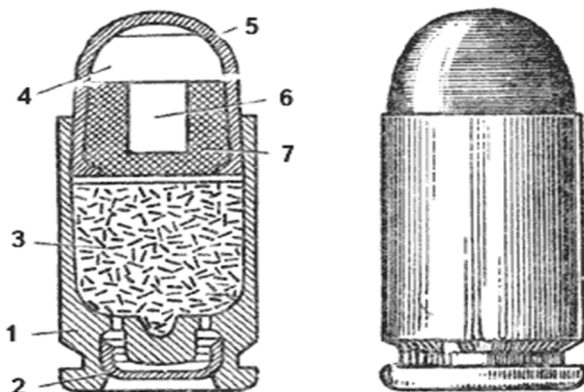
Общий вид 9 мм пистолетного патрона и его устройство: 1 – гильза; 2 – капсюль; 3 – пороховой заряд; 4 – пуля; 5 – биметаллическая (плакированная) оболочка; 6 – стальной сердечник; 7 – свинцовая рубашка
